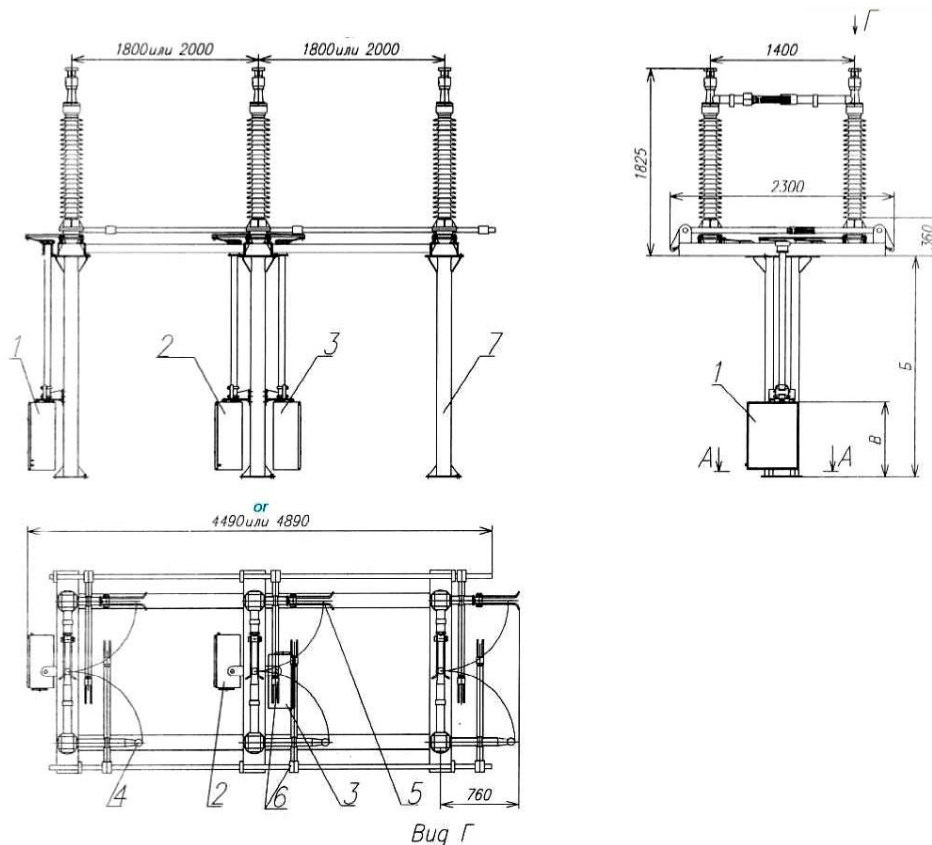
Габаритные и установочные размеры разъединителя РПД-110:
